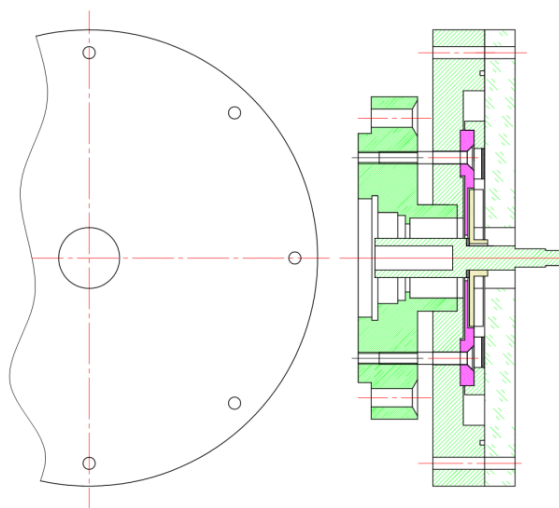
Схема размещения колеса d45 в корпусе турбинного узла
